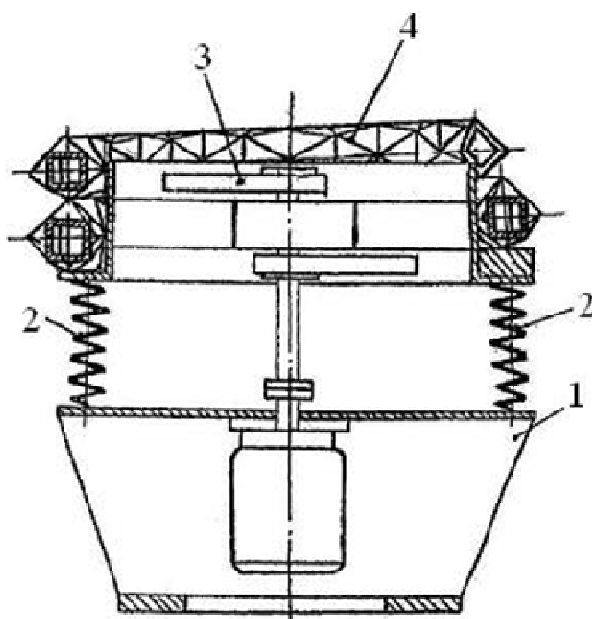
Малогабаритная установка для приготовления кормов
